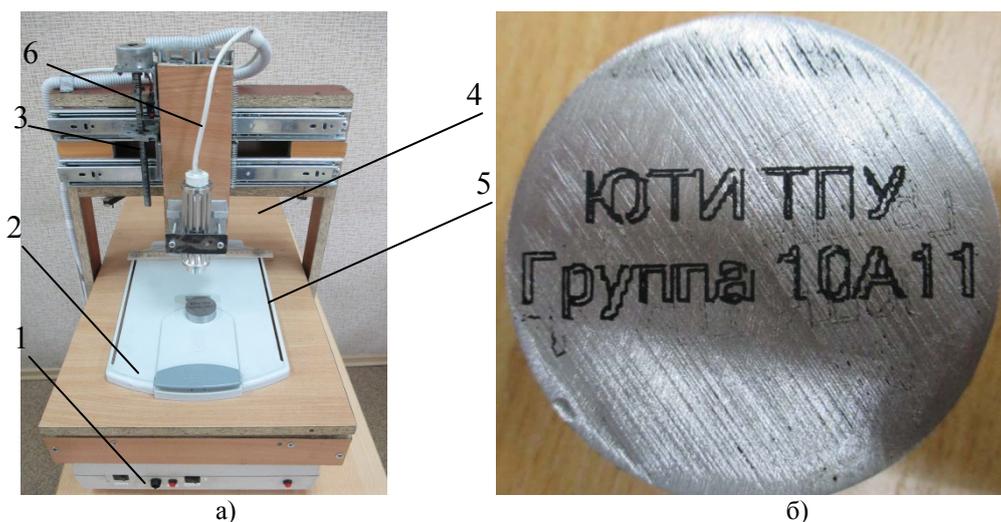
Общий вид станка с ЧПУ для маркировки лазером и образец с нанесенной маркировкой
